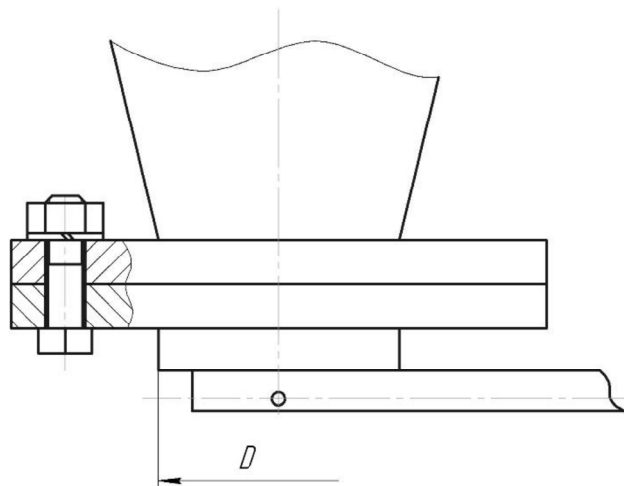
Схема для розрахунку болтового з'єднання шарового затвору
